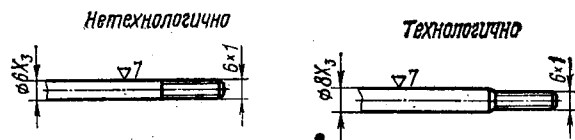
Размеры сопрягаемых шлифуемых и резьбовых поверхностей.
